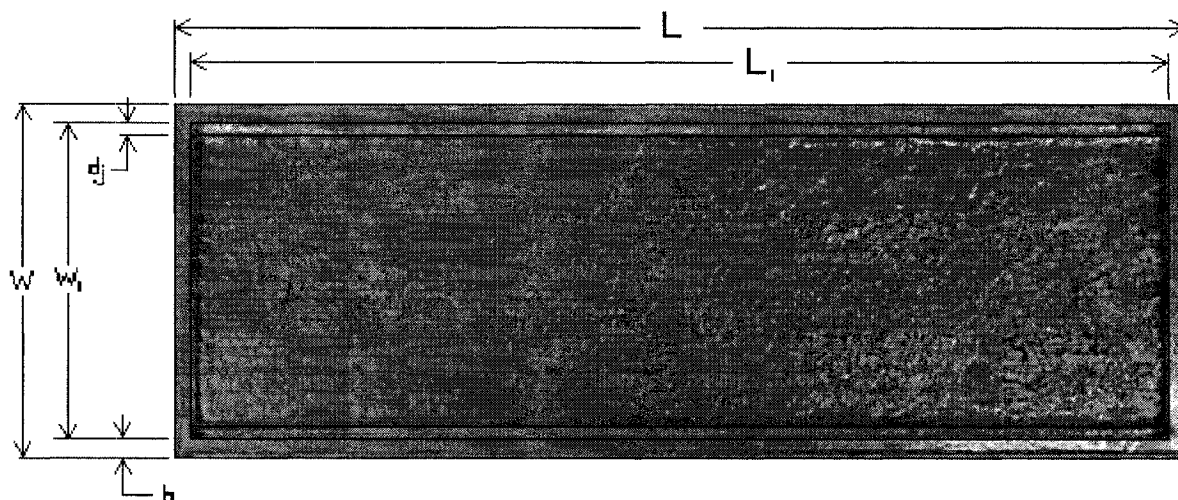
Vue de dessus de la pièce avec les dimensions.
